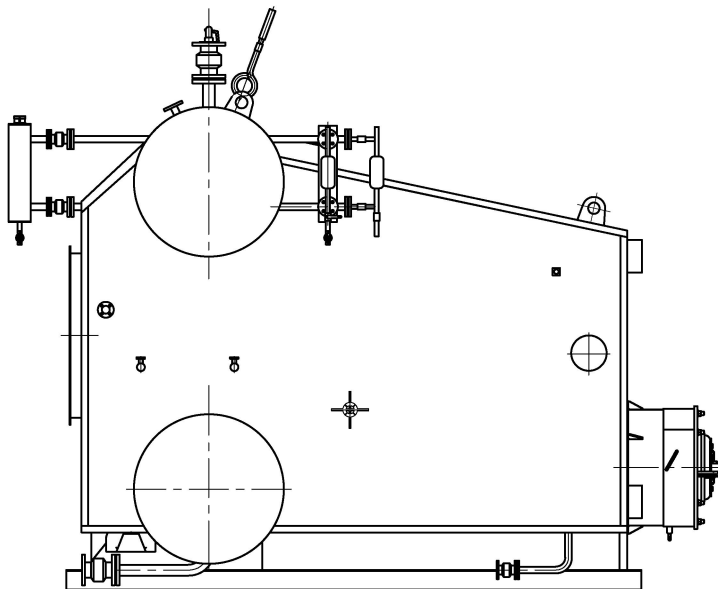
Общий вид котла Е-1,0-0,9 с устройством топочным 19-01-06-000-1 специальной конструкции для нефтегазовой отрасли.
